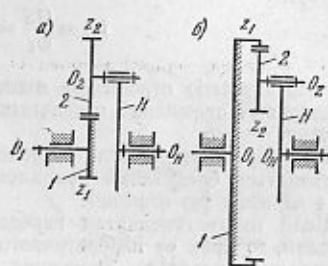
Элементарная планетарная передача: а) колеса с внешним зацеплением, б) колеса с внутренним зацеплением.
